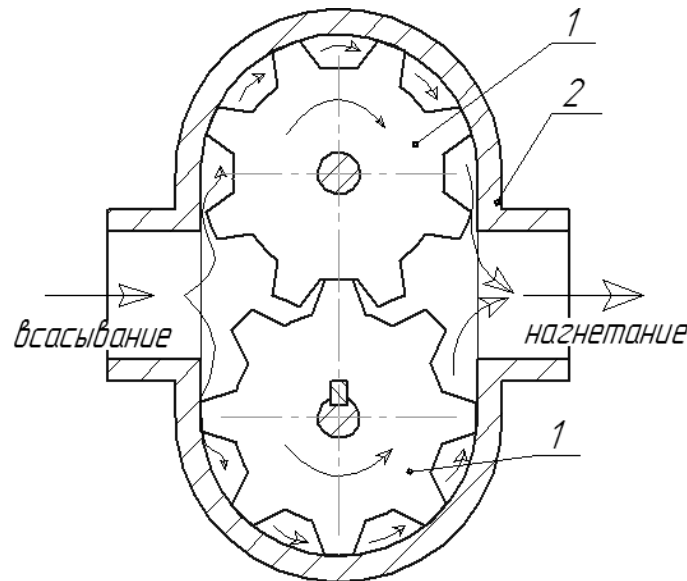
Шестеренный насос: 1 – зубчатые колеса; 2 – кожух
